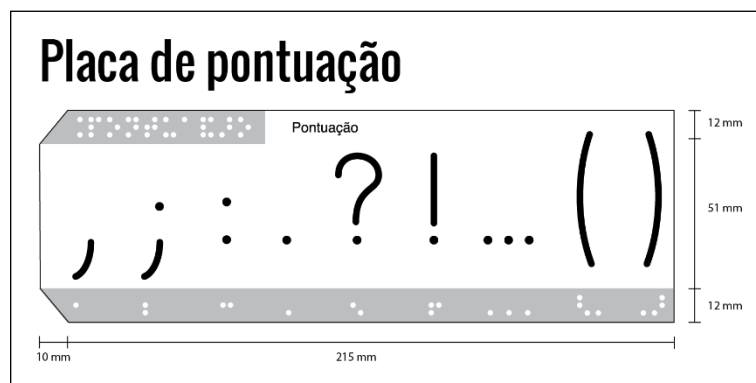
Desenho técnico da placa de pontuação (fonte: a autora)
